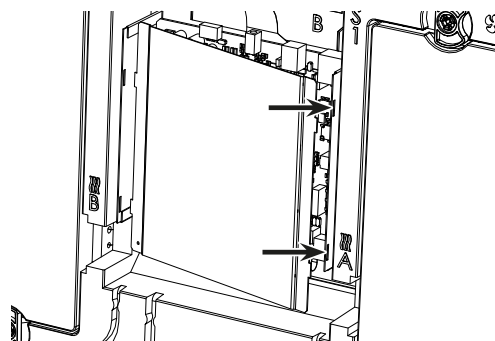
HCV 400-460: Hovedprintplade lægges fri
